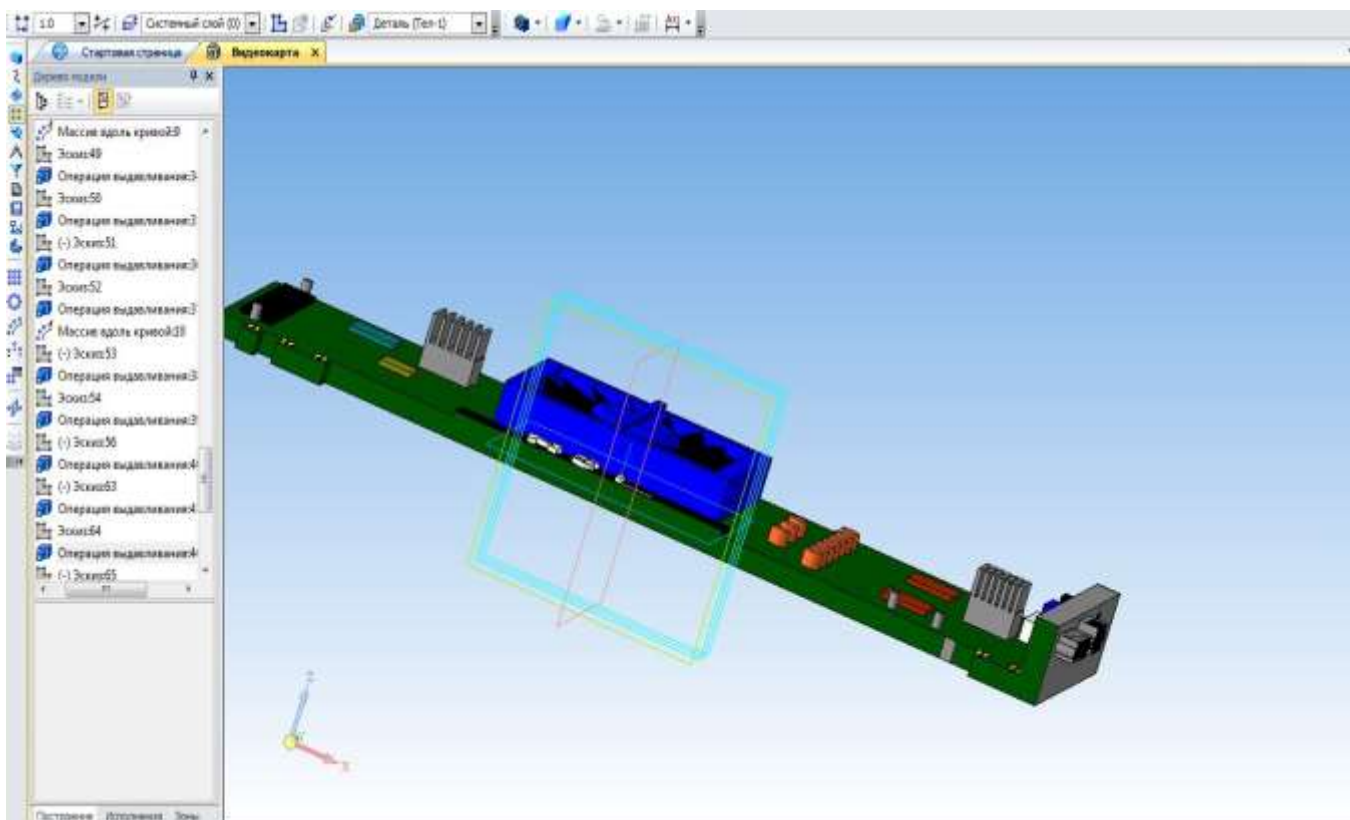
«3D сборка системного блока ПК», 3D сборка - видеокарта
